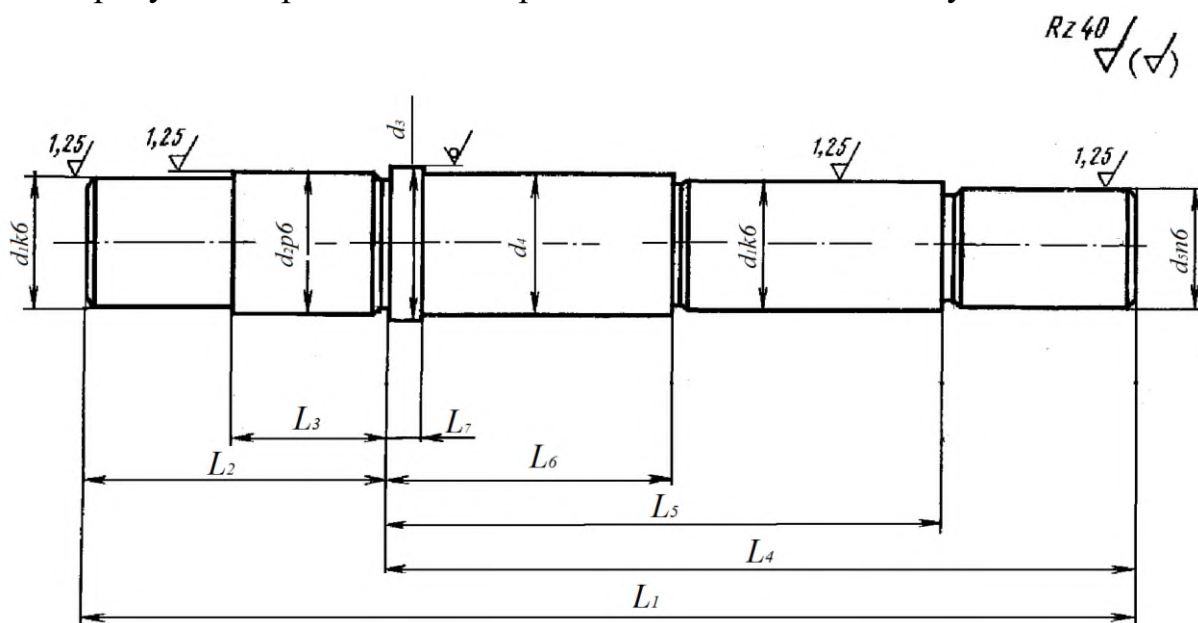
Эскиз вала редуктора привода технологической машины (задание)
